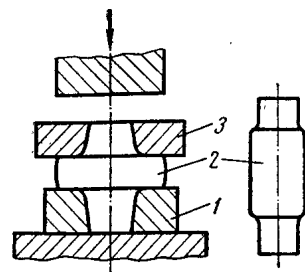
Схема высадки средней части заготовки при ковке под молотом или прессом: 1, 3 — кольца, 2 — заготовка
